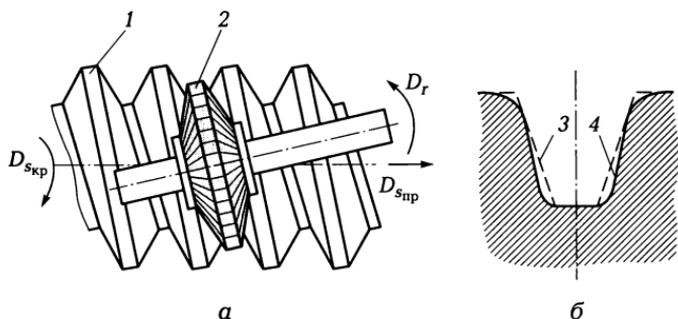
Резьбофрезерование дисковой фрезой:
